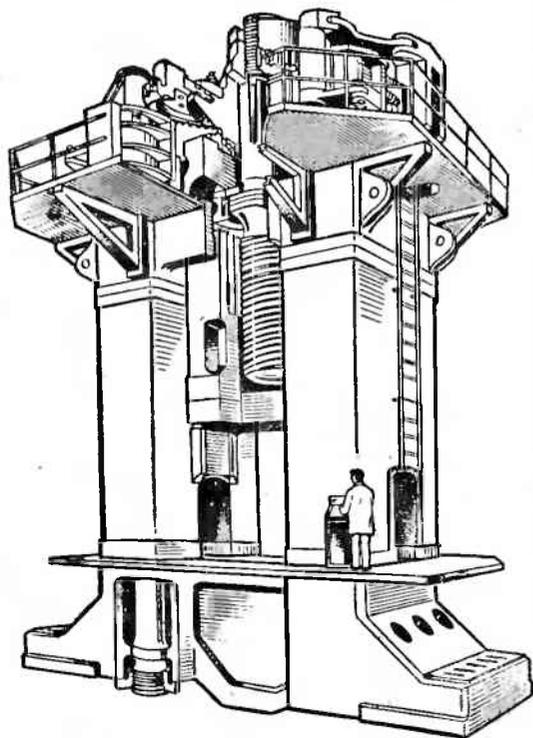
Винтовой пресс с шестеренным приводом усилием 8000 тс
